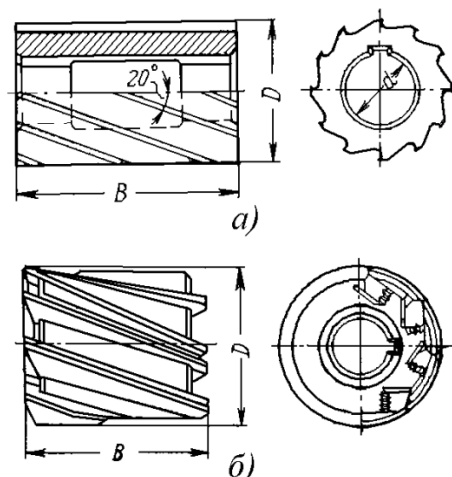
Цилиндрические фрезы: а – с мелким зубом; б – со вставными ножами.
